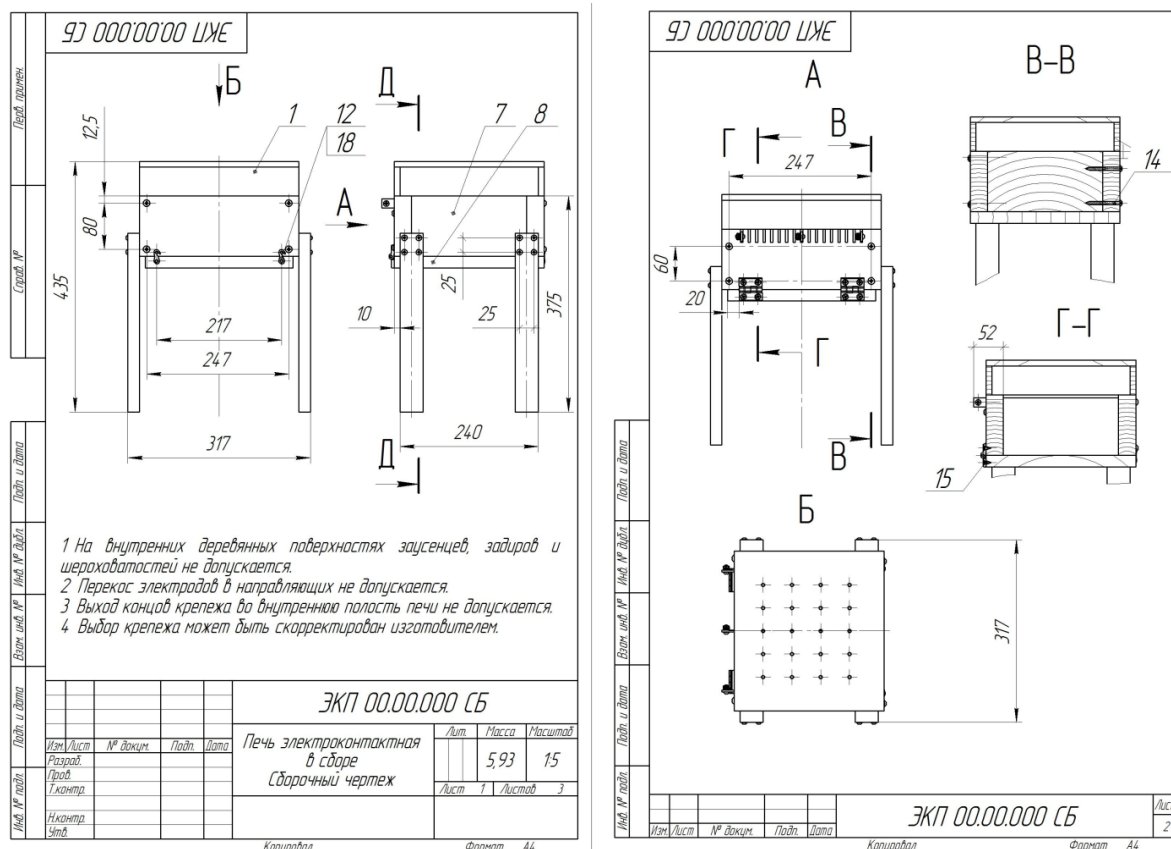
Фрагмент конструкторской документации лабораторного образца
